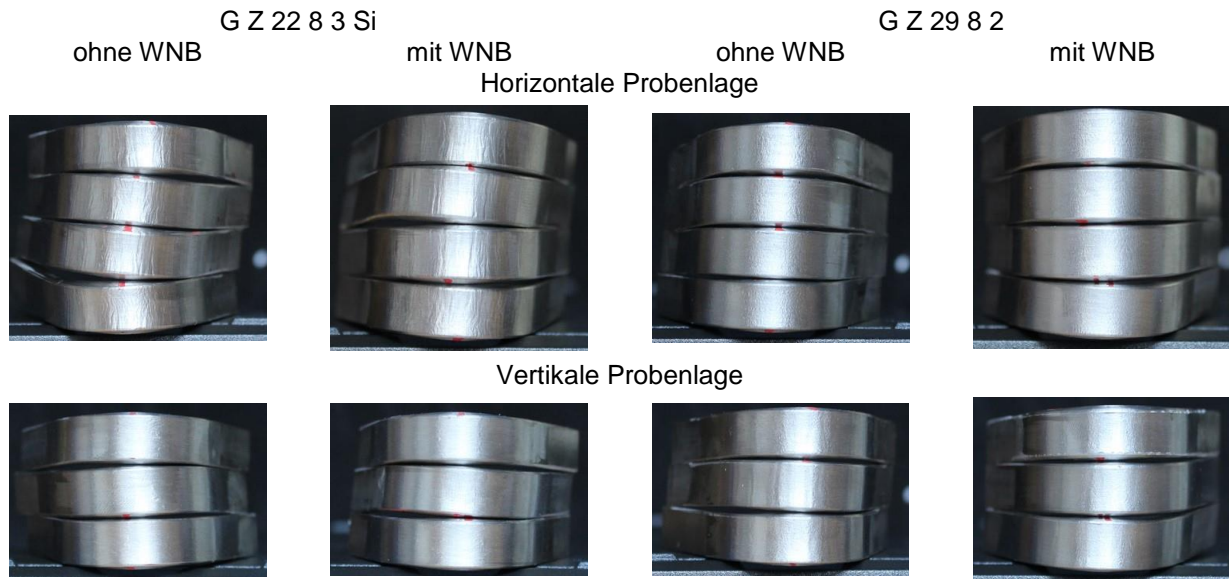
Biegeproben der Schweißgüter des G Z 22 8 3 Si und des G Z 29 8 2 im Schweißzustand und im wärmebehandelten Zustand weisen keine inneren Unregelmäßigkeiten auf
